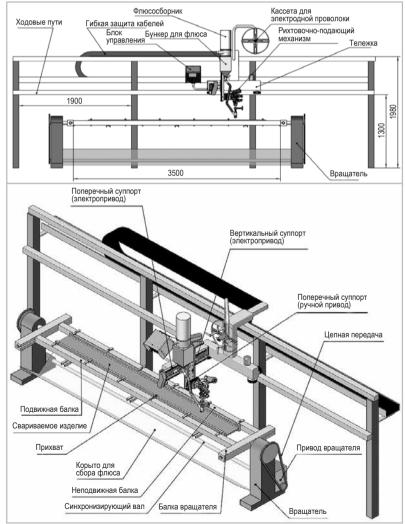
Установка для сварки двутавровых балок спекательных тележек — общий вид и комплектация
